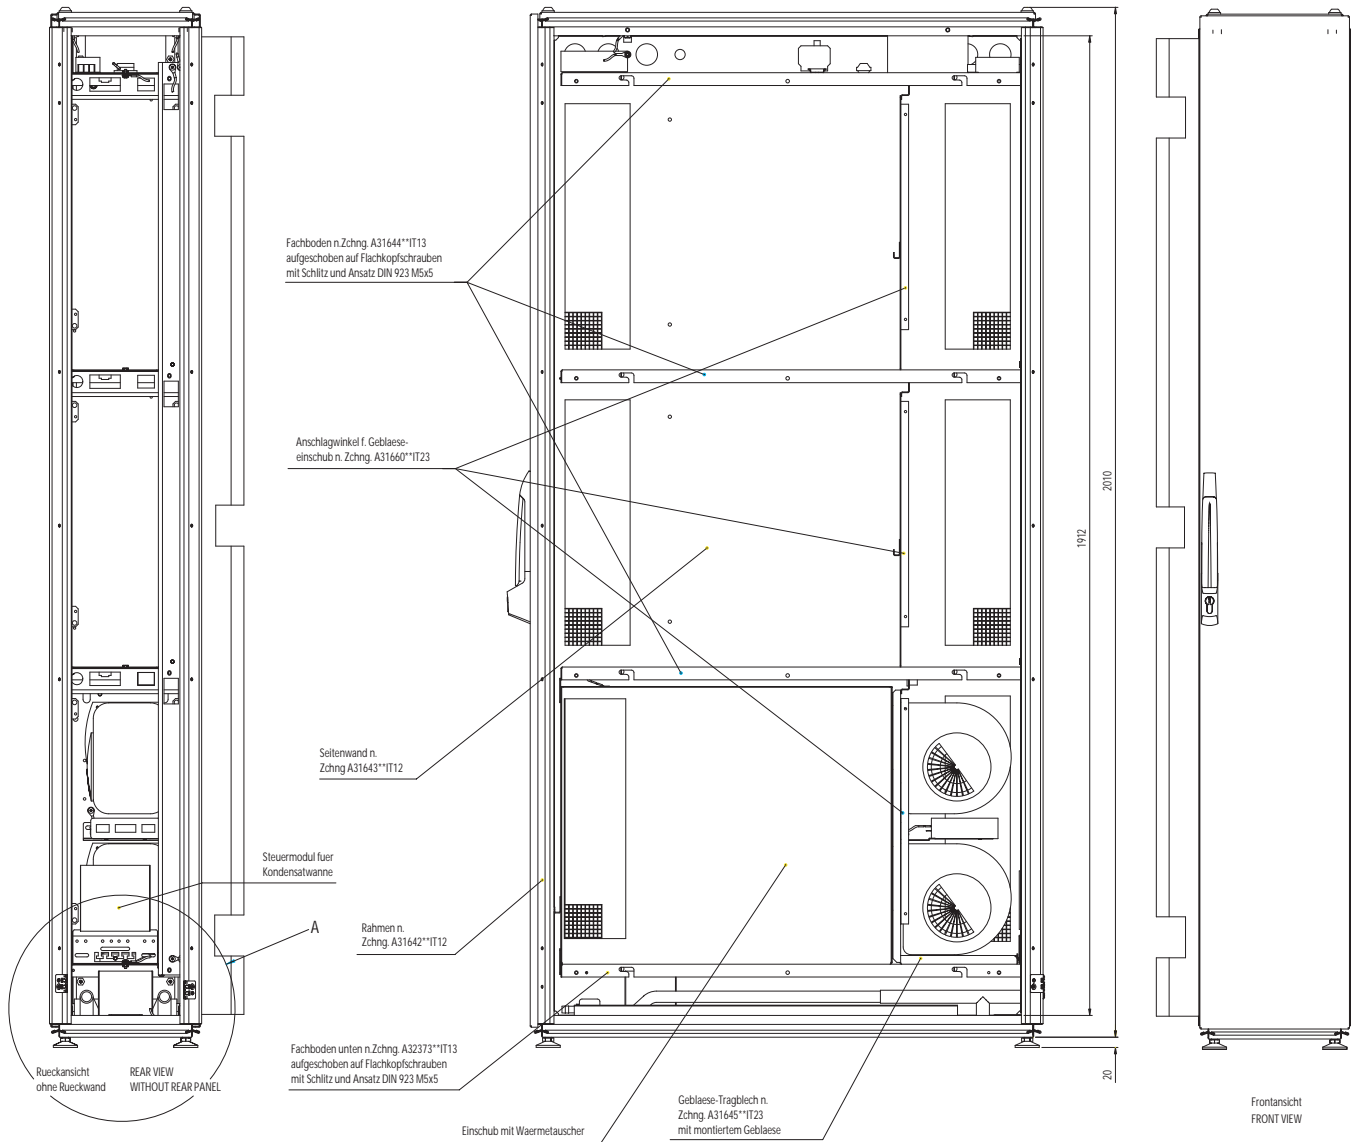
Übersichtzeichnung - Liquid Cooling Package (Vorder-, Seiten- und Rückansicht)
